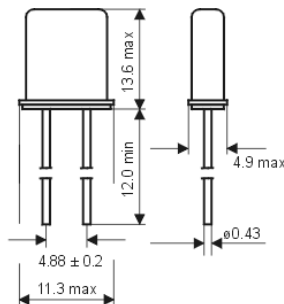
Габаритні розміри кварцового резонатора НС-49S - 32768 Гц
